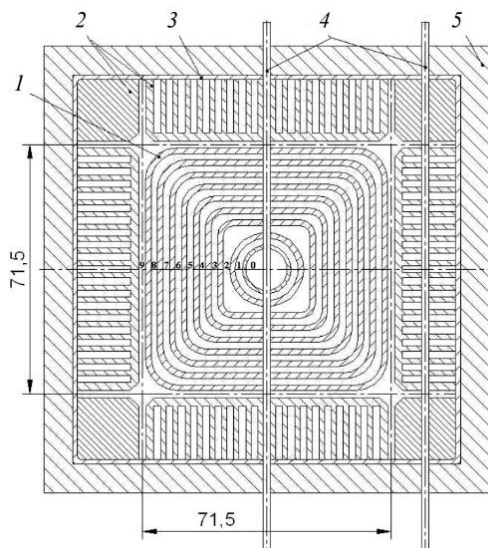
Поперечный разрез колонки гидравлического стенда:
